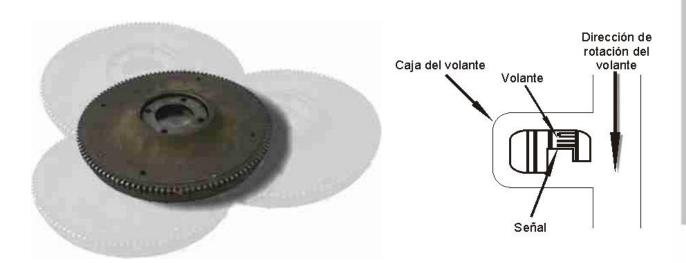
EL VOLANTE Y EL HUECO DE INSPECCIÓN DE LA CAJA DEL VOLANTE
